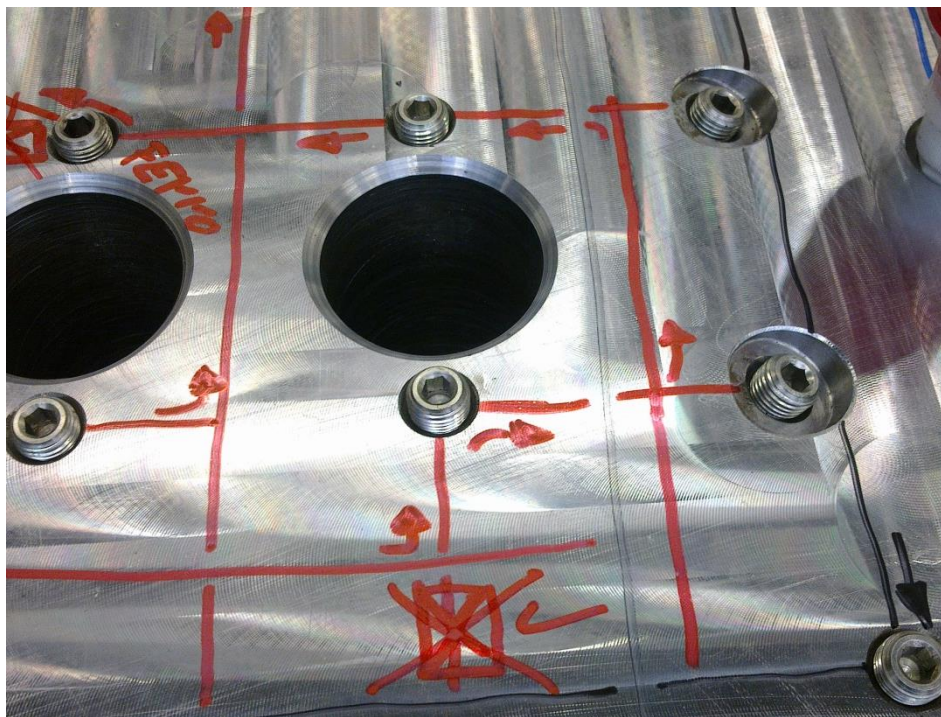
Sistema de refrigeração desenhado na peça (Imagem do Autor)
